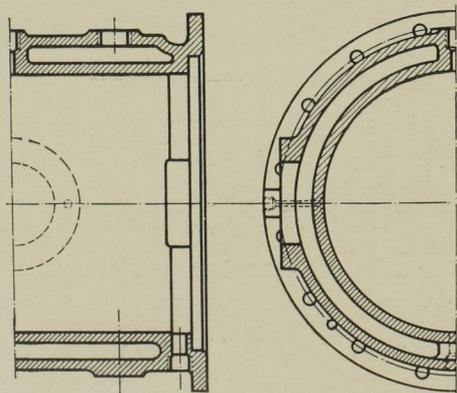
Niederdruckzylinder. Massst. 1:16.
